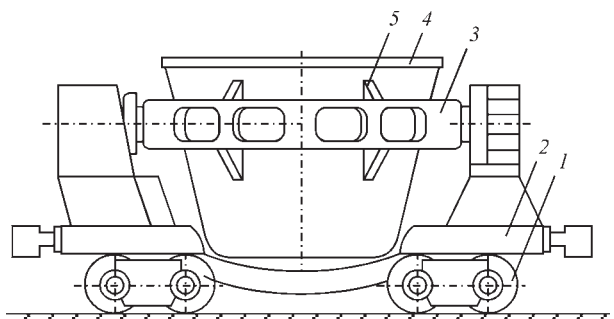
Схема шлаковоза: 1 — ходовая часть шлаковоза; 2 — платформа шлаковоза; 3 — опорное кольцо для чаши; 4 — чаша шлаковоза; 5 — опорные элементы на чаше
